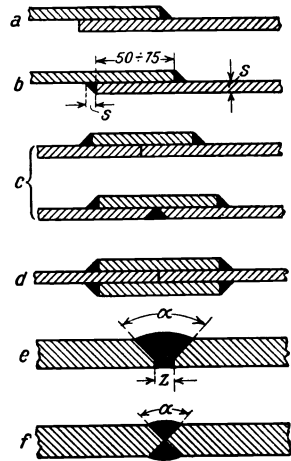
Vorbereitung elektrischer Lichtbogen-Blechschweißungen.
